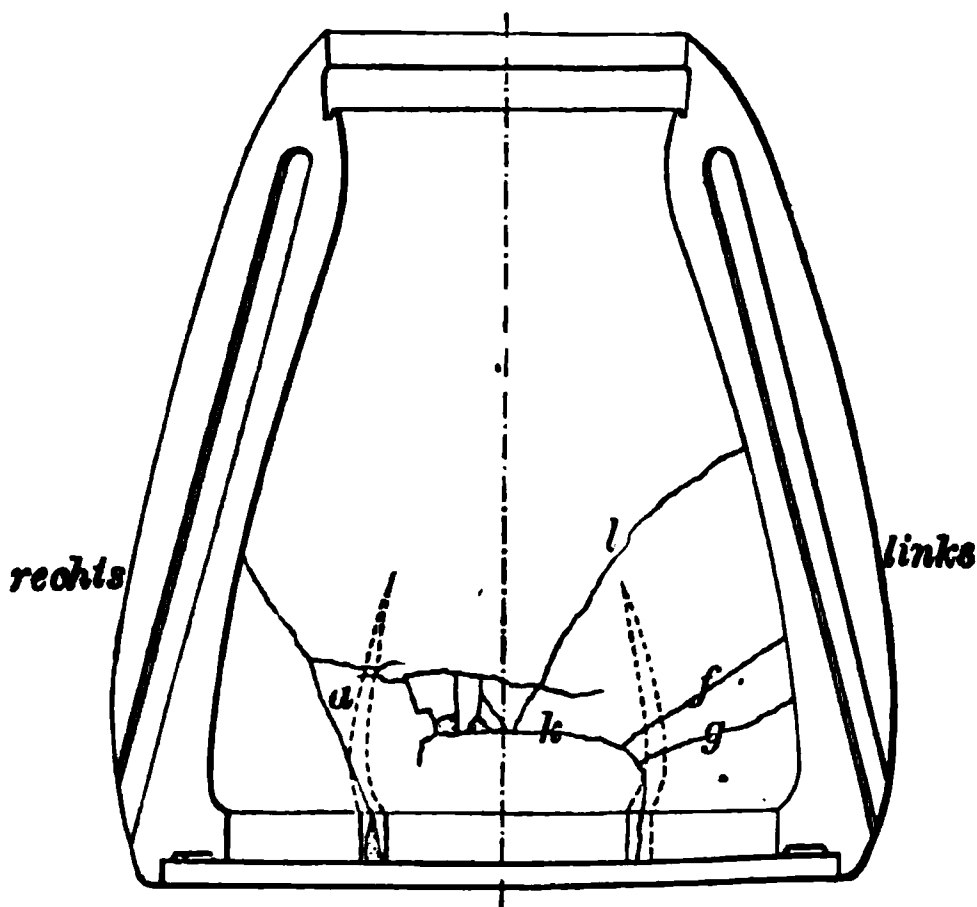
Revers de la plaque de cuirasse après le troisième coup.
